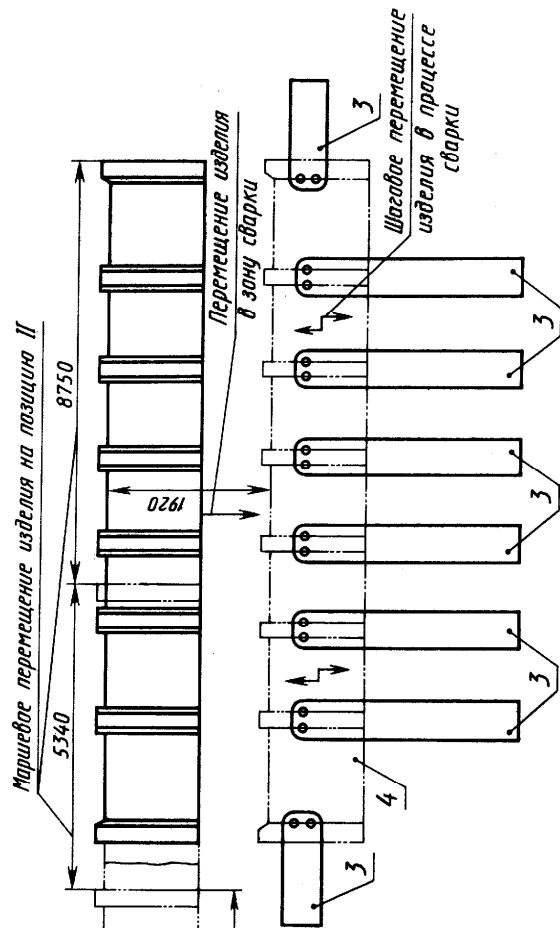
Схема участка контактной сварки боковых стенок
